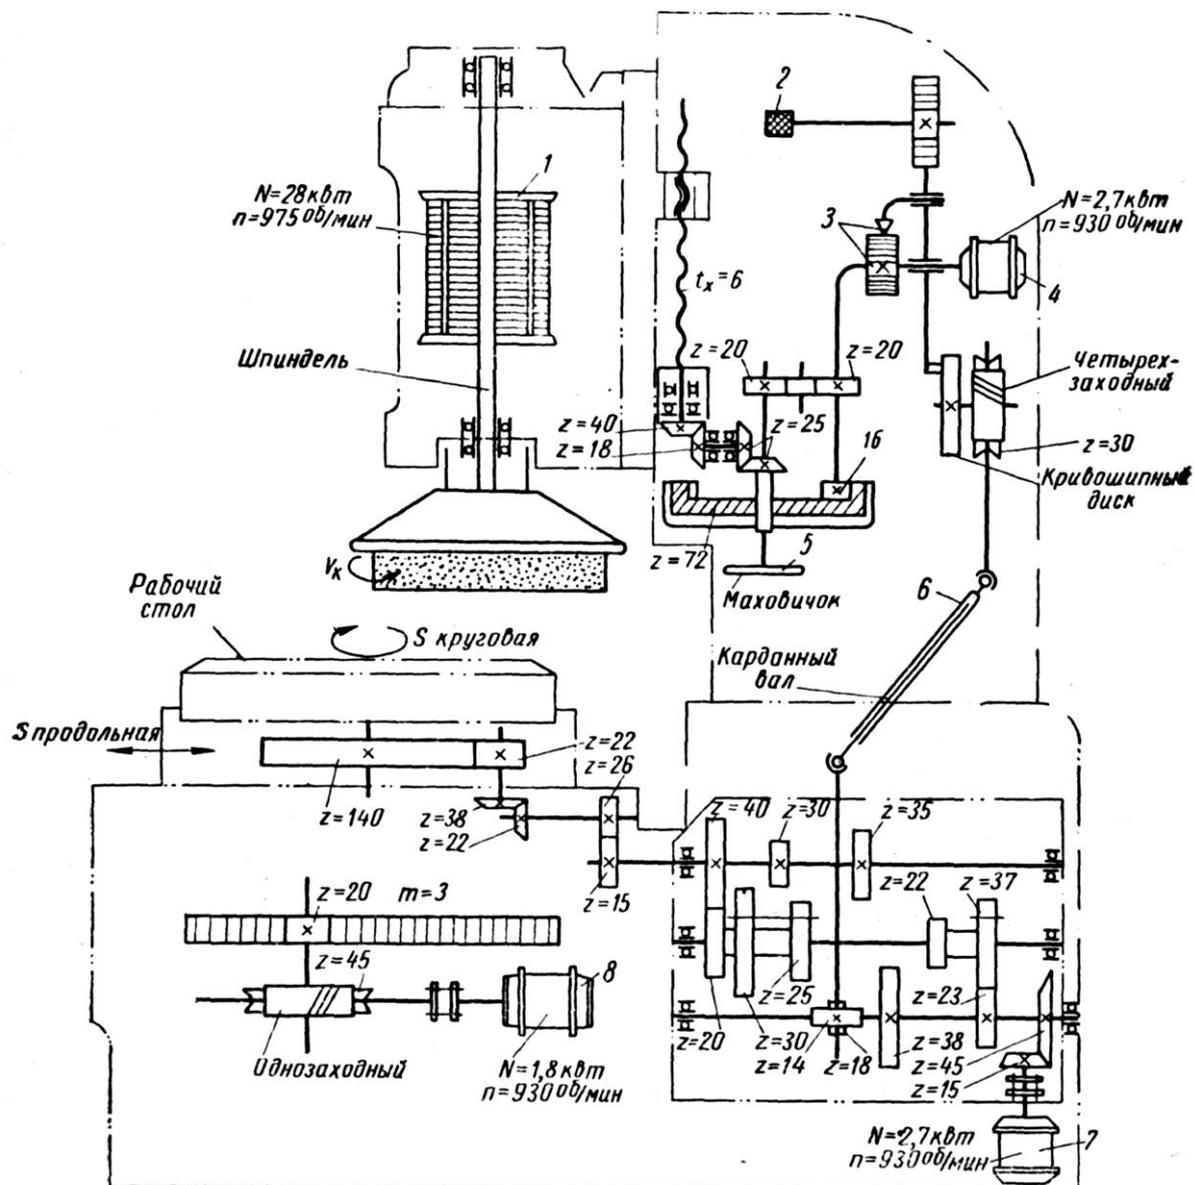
Кинематическая схема плоскошлифовального станка модели 3756, работающего торцевым кругом
